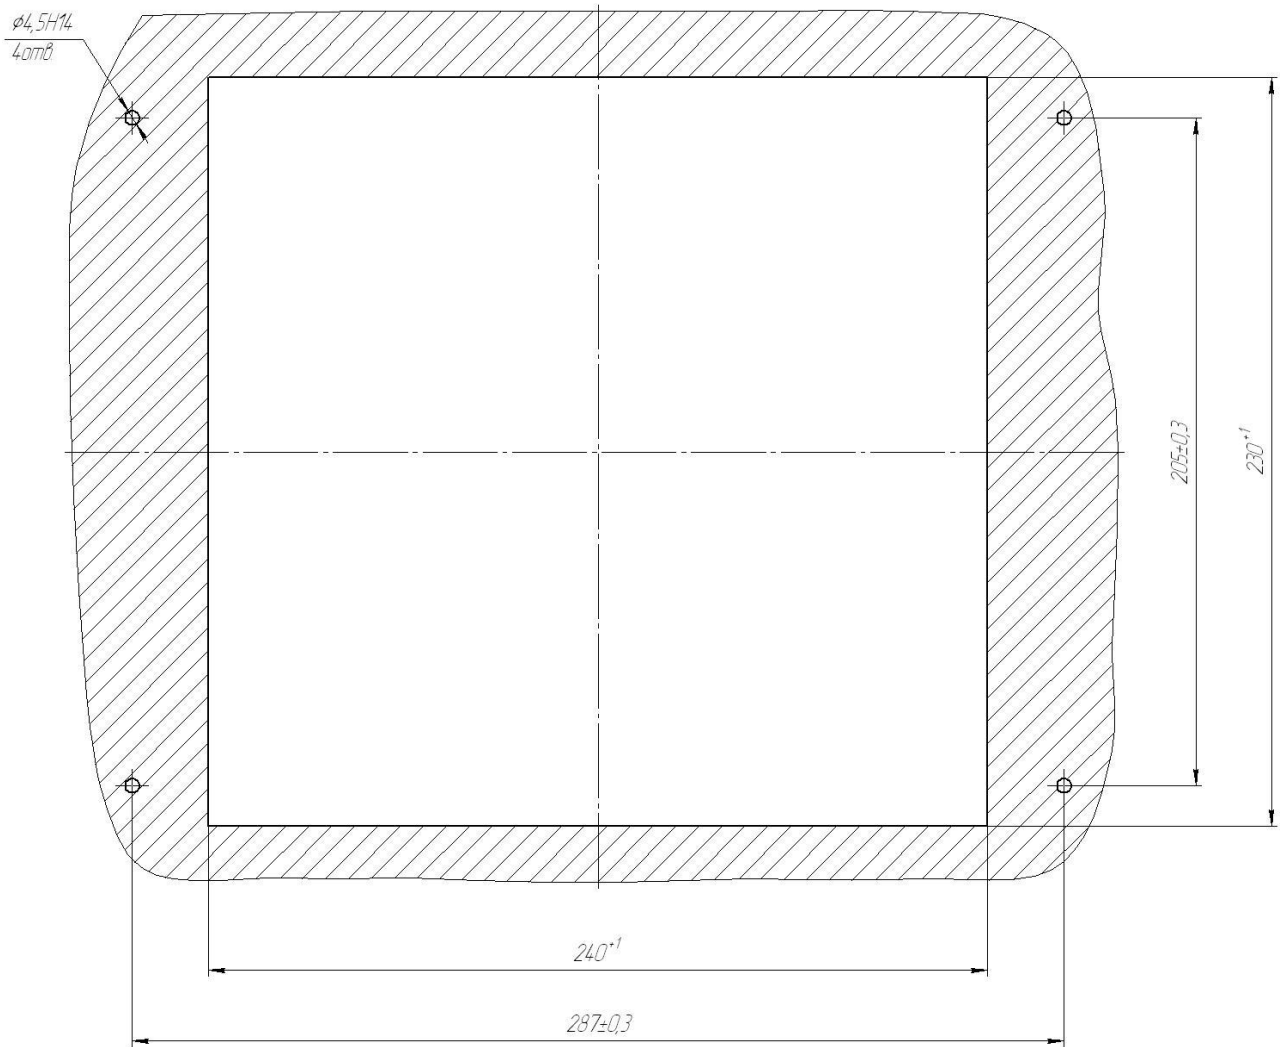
Габаритные размеры окна и крепежных отверстий для установки РЗЛ-05 Ш1 ЦС
